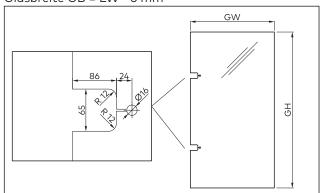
Glasbearbeitungen für die Wandbefestigung mit aufliegender Montageplatte
